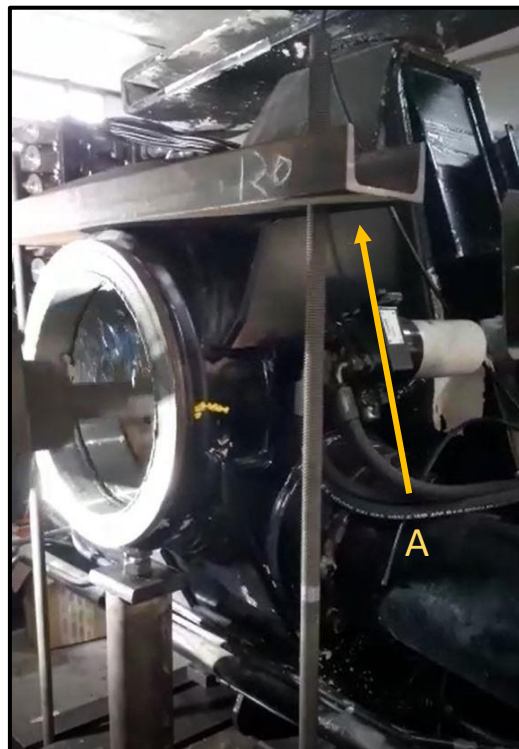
Detalle de viga de sujeción (A). Fuente: Foto cedida al autor.
